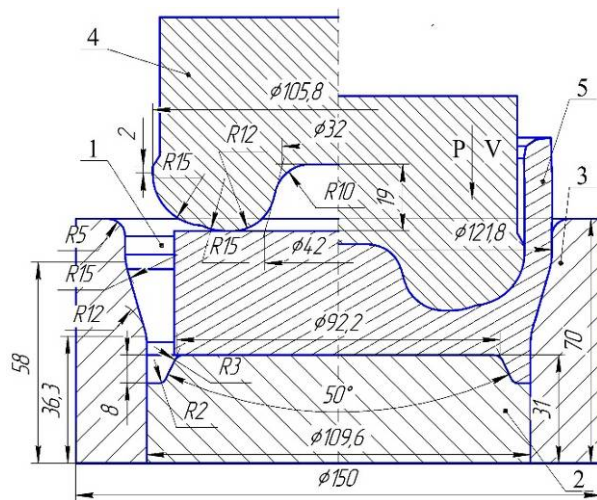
Схема зворотного видавлювання: 1 – заготовка, 2 – плита, 3 – матриця, 4 – пуансон, 5 – напівфабрикат
